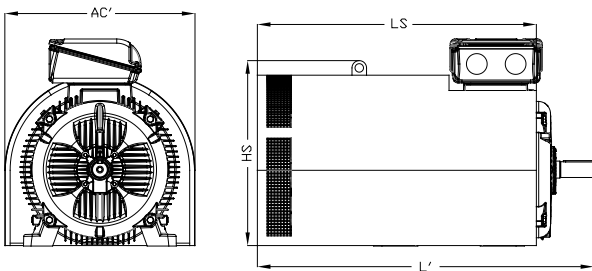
Maßzeichnung für Motoren mit Horizontierschrauben und Passstiften
